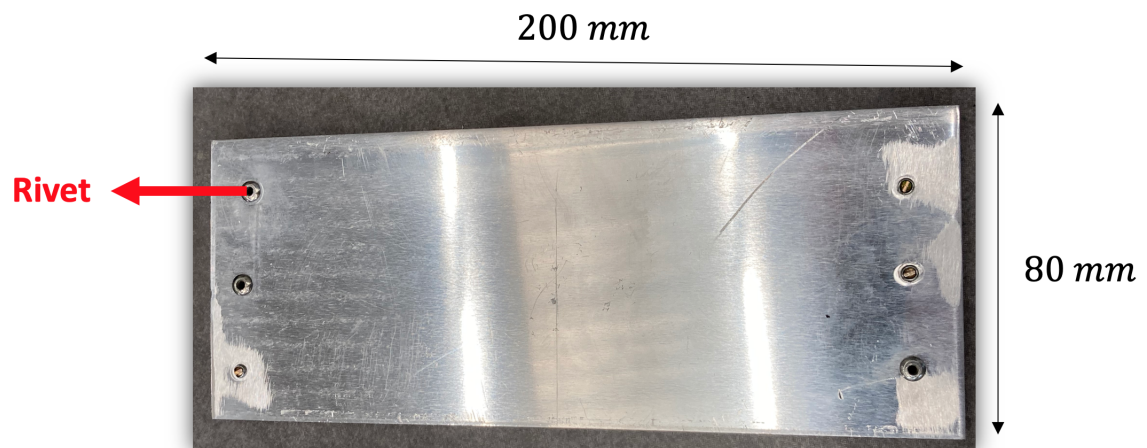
Vue du haut du spécimen empilé en structure sandwich à 3 couches avant laminage.
